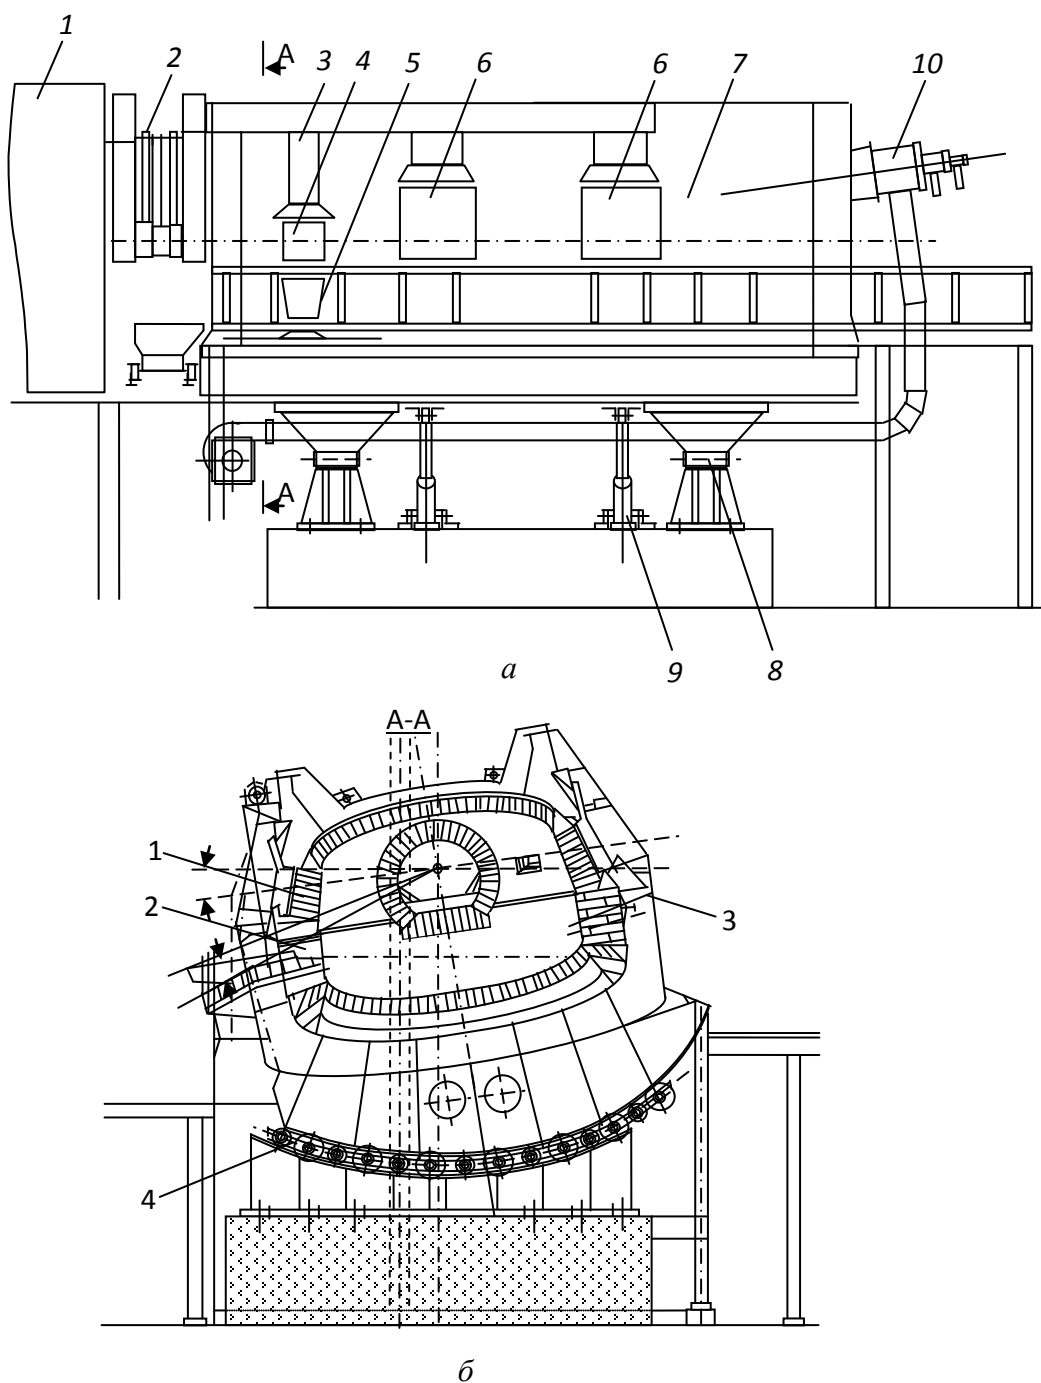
Наклоняющаяся печь «Мерц»: *а* – общий вид: 1 – шлаковая камера; 2 – газоход шарнирный; 3 – отсос газа; 4 – шлаковое окно; 5 – мульда; 6 – загрузочные окна; 7 – корпус печи; 8 – опоры печи; 9 – гидроцилиндры поворота; 10 – горелка; *б* – разрез А-А: 1 – печь; 2 – шлаковое окно; 3 – узел фурмы; 4 – поворотный узел печи
